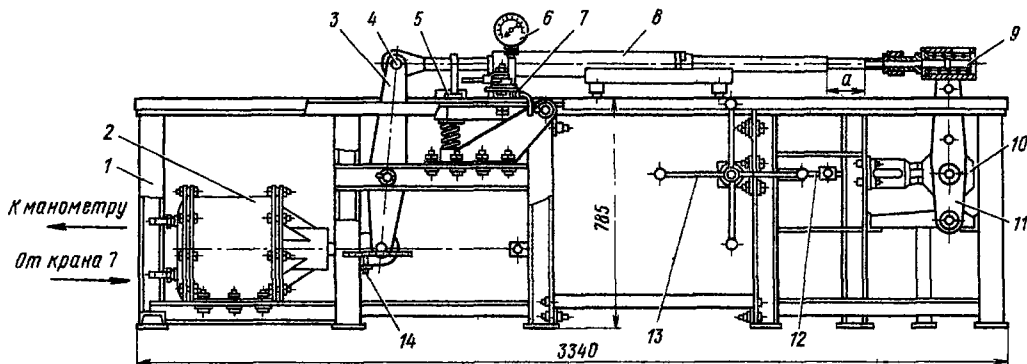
Схема стенда для испытания автоматического регулятора тормозной рычажной передачи:
